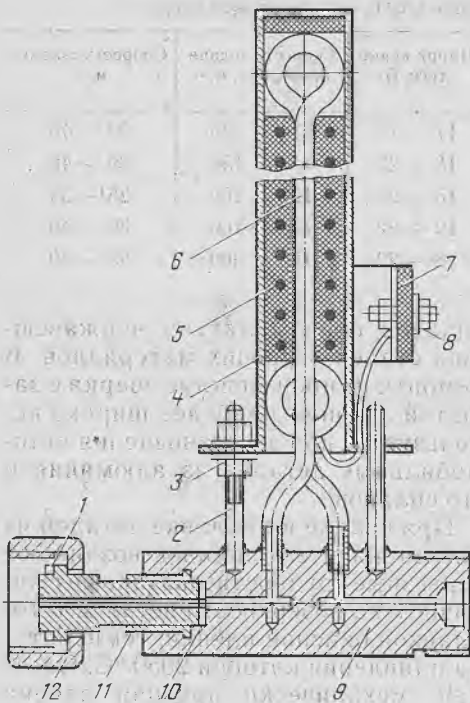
Подогреватель углекислого газа: 1 и 10 — прокладки; 2 — стойка; 3 — гайка; 4 — кожух; 5 — нагревательная спираль; 6 — змеевик; 7 — панель; 8 — зажим подогревателя; 9 — штуцер; 11 — патрубок; 12 — накидная гайка
